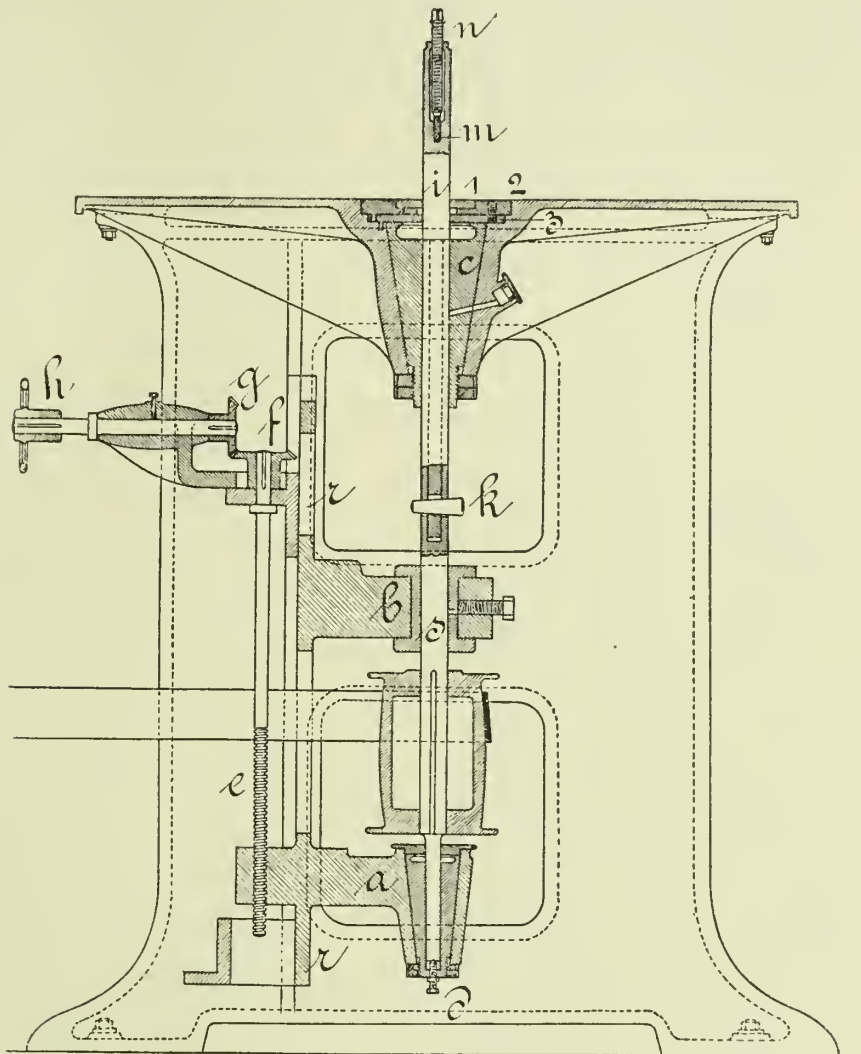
Senkrechter Schnitt einer Kehlmaschine.
